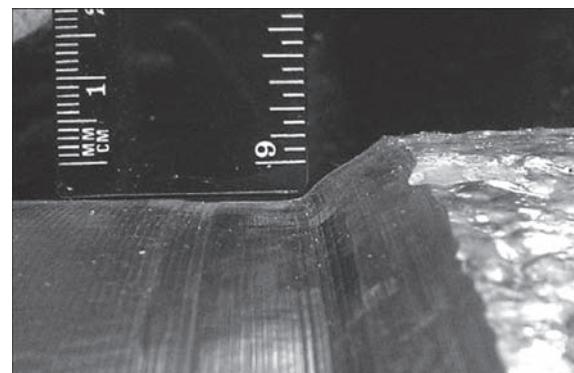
Глубина обработки поверхности слитка титанового сплава на токарном станке
